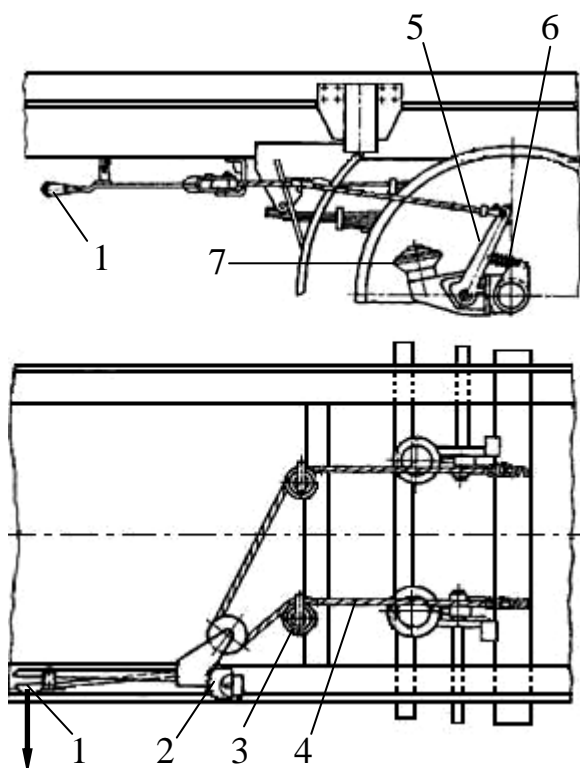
Конструкция стояночного тормоза прицепа КАМАЗ: 1 – рычаг; 2 – зубчатый сектор; 3 – ролик; 4 – трос; 5 – приводной рычаг; 6 – оттяжная пружина; 7 – тормозная камера
